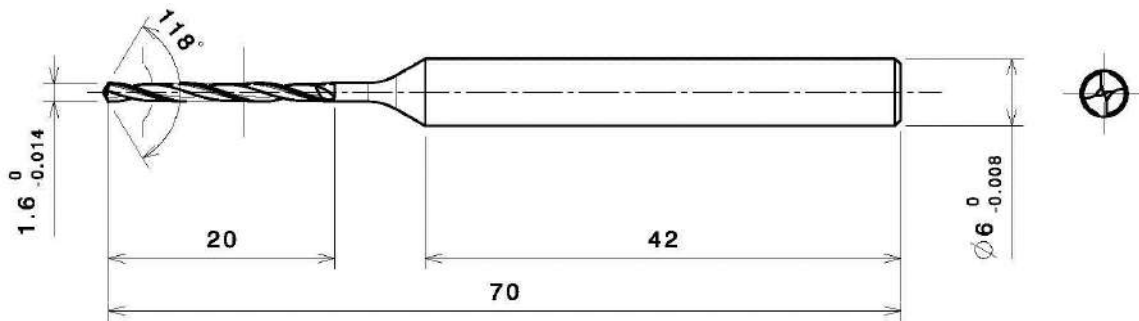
Креслення твердосплавної фрези SSD D1.6X20FX 70-6 зі сплаву UF10
